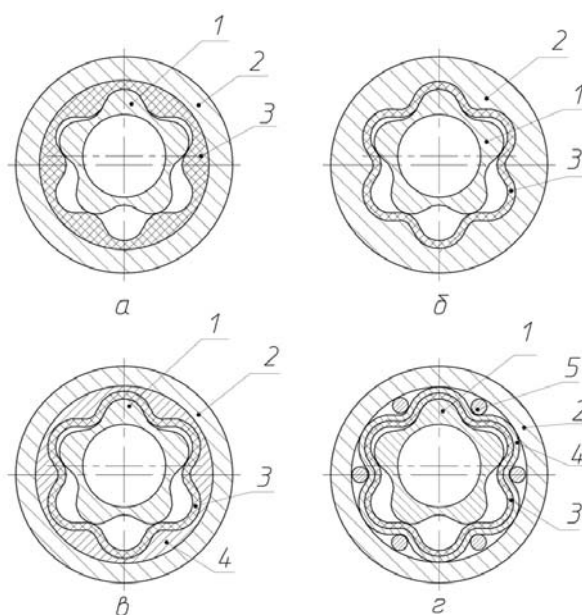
Торцовое сечение героторных механизмов (варианты исполнения): 1 – ротор; 2 – корпус статора; 3 – резиновая обкладка; 4 – вкладыш (литой или кованный), зубчатая тонкостенная оболочка; 5 – пруток
